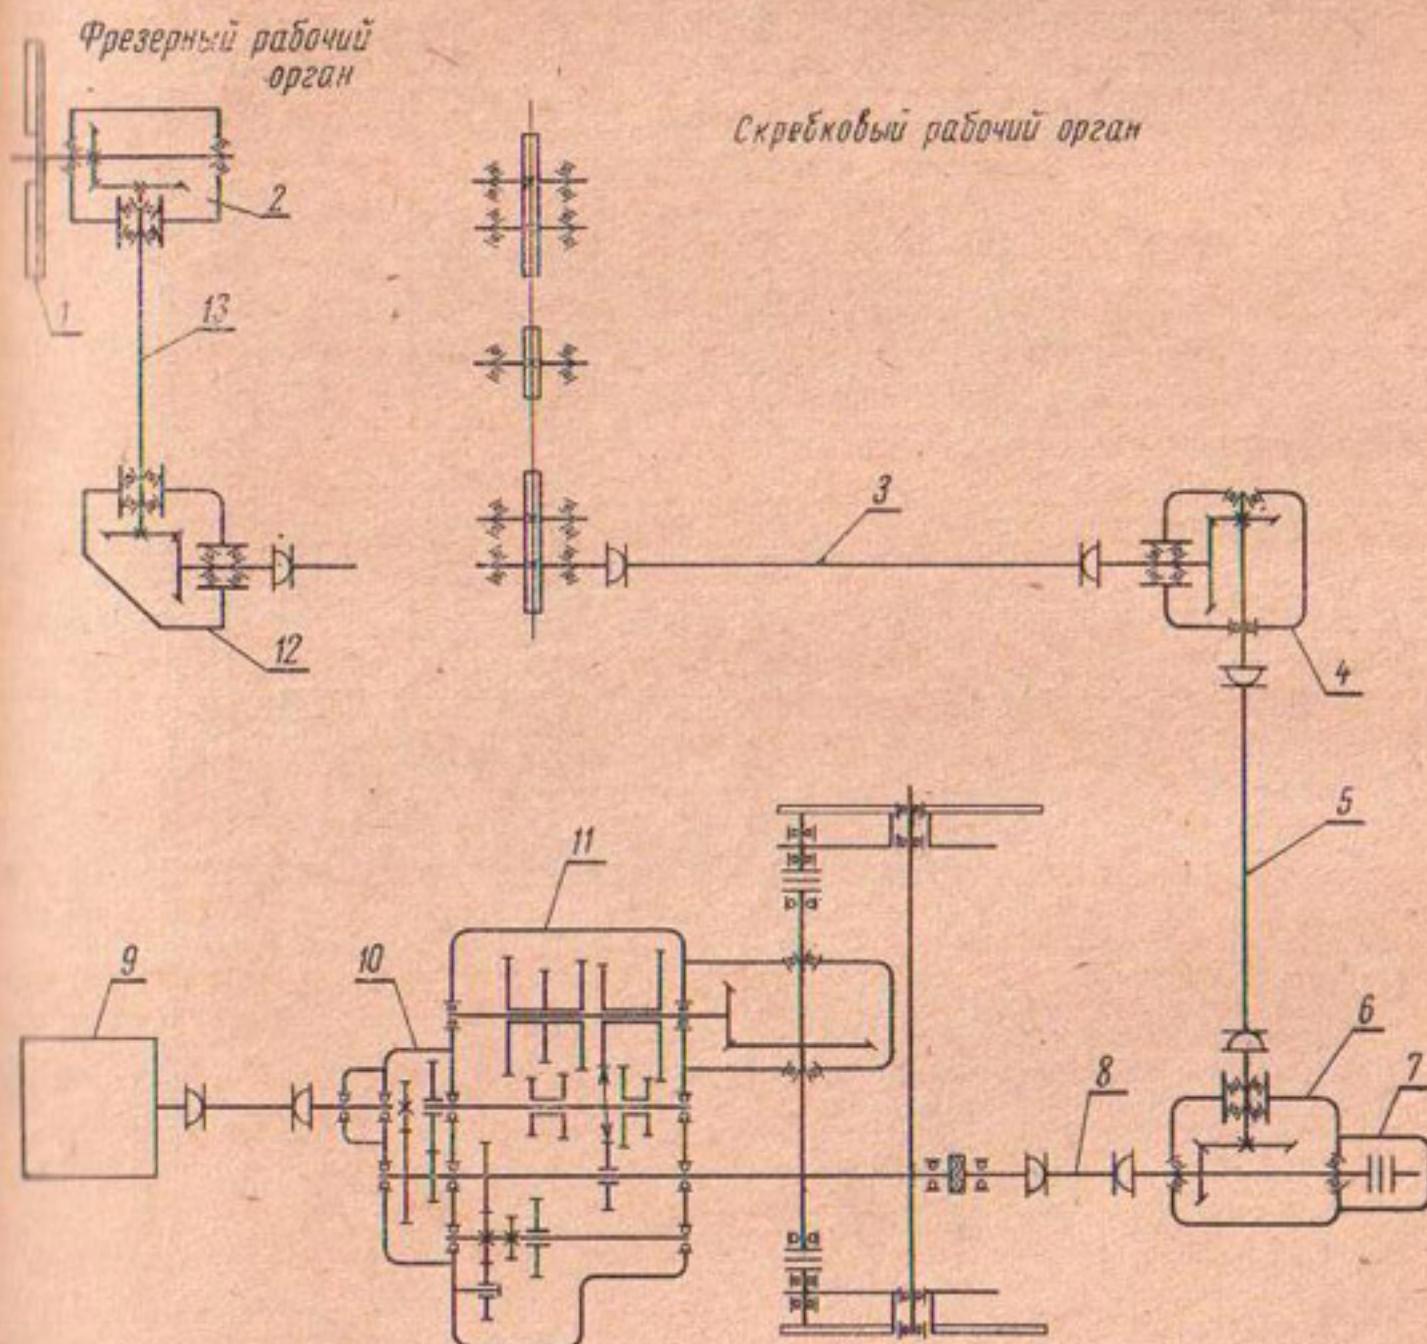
Кинематическая схема каналоочистителя Д-490М:
